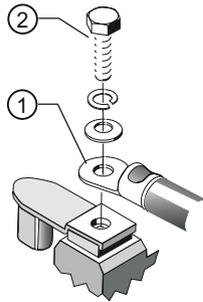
Anschluss mit Kabelschuh und Befestigungsschraube (Prinzipdarstellung)
